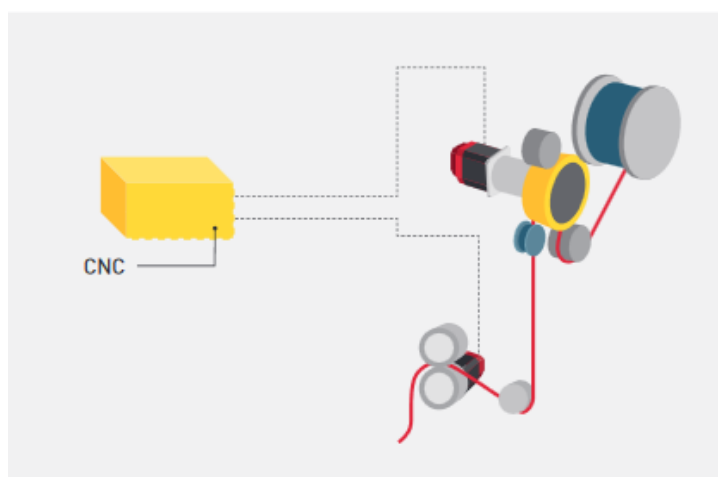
Systém automatického návleku drôtu (AWT) [21].
